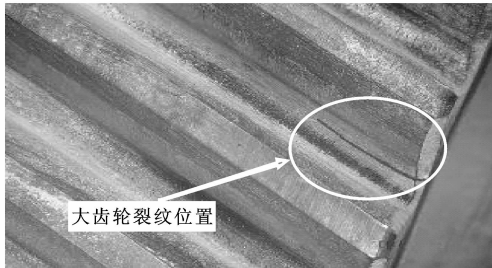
机车走行部齿轮箱大齿轮的早期裂纹
